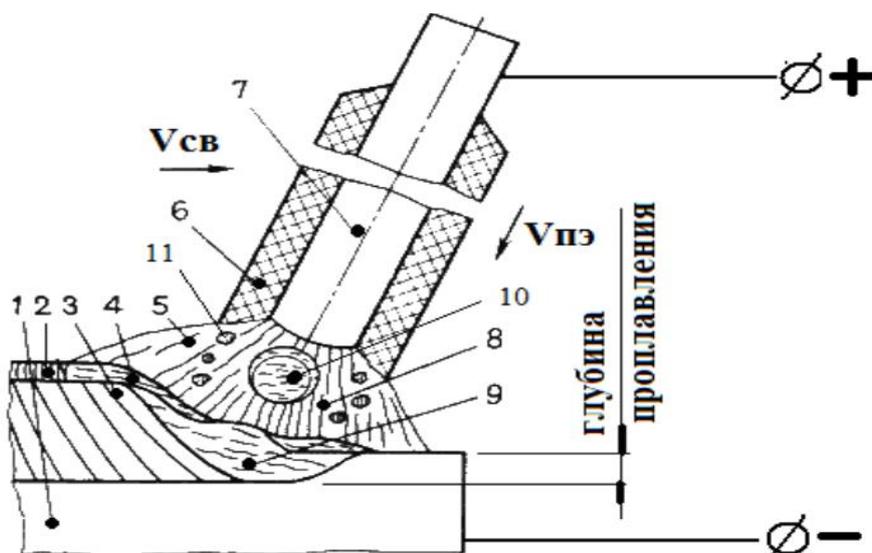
Схема ручной дуговой сварки покрытым электродом (РДС):
